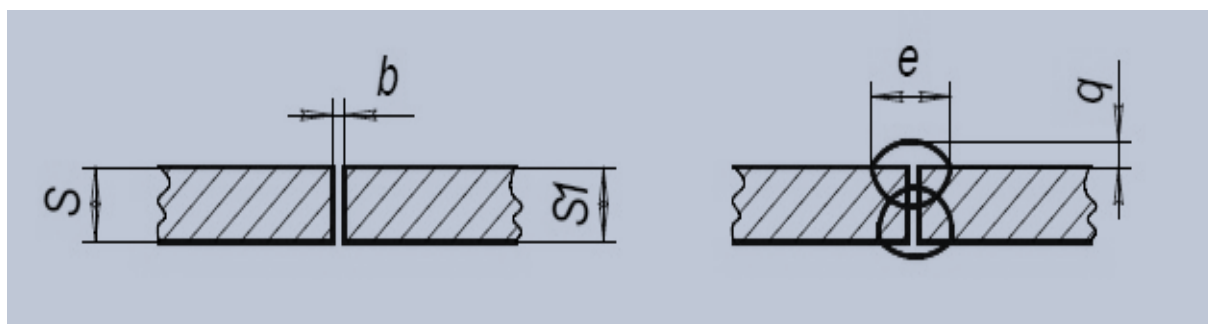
Зварне з'єднання С7 для зварювання поздовжнього шва
